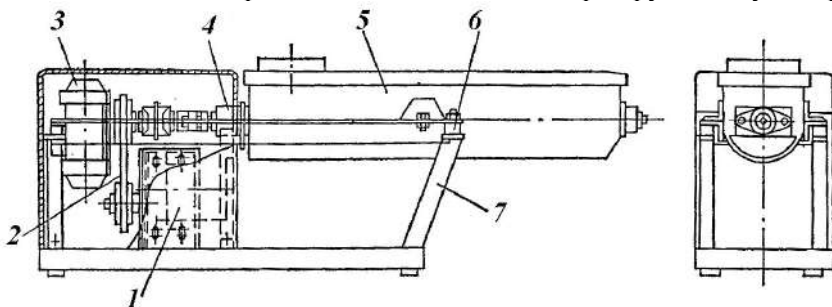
Лопастной вибрационный смеситель: 1 – электродвигатель; 2 – клиноременная передача; 3 – вибровозбудитель; 4 – лопастной вал; 5 – желоб; 6 – упругая опора; 7 – опорная рама.
